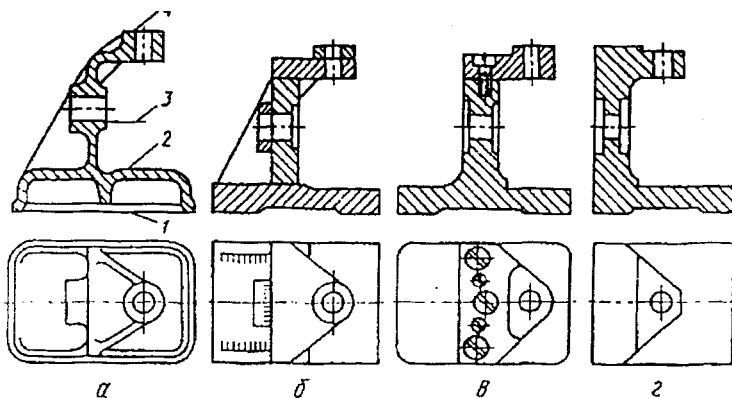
Варианты конструкции корпуса кондуктора при изготовлении его из различных видов заготовок
